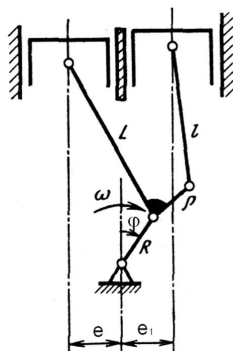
Дезаксиальный кривошипно-шатунный механизм с прицепным шатуном и параллельными осями главного и бокового цилиндров
